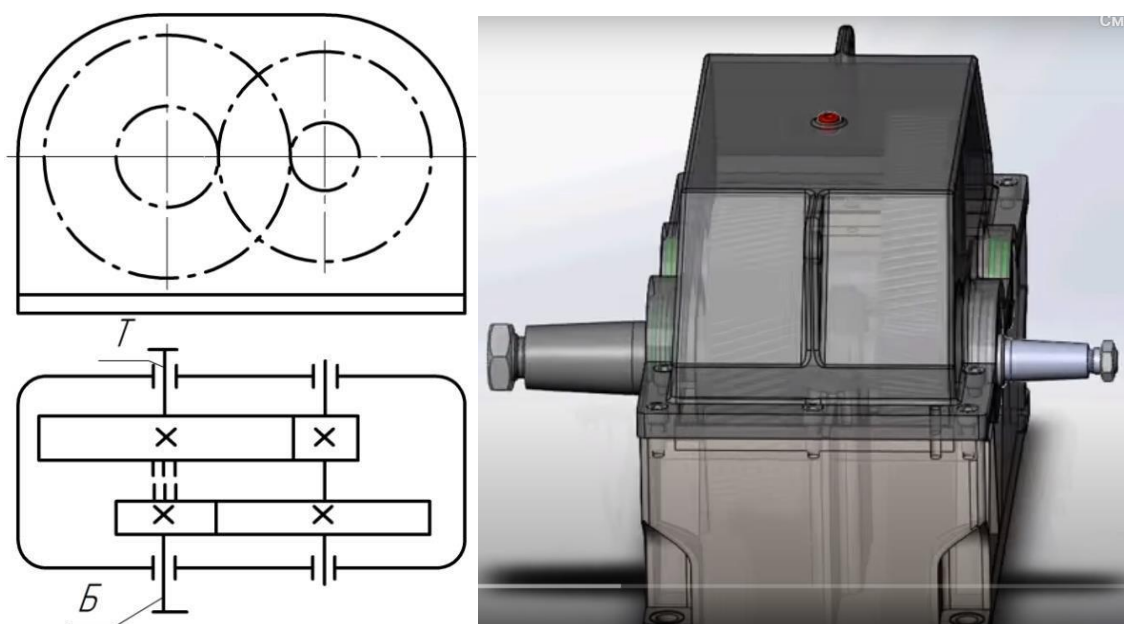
Двухступенчатый горизонтальный редуктор
